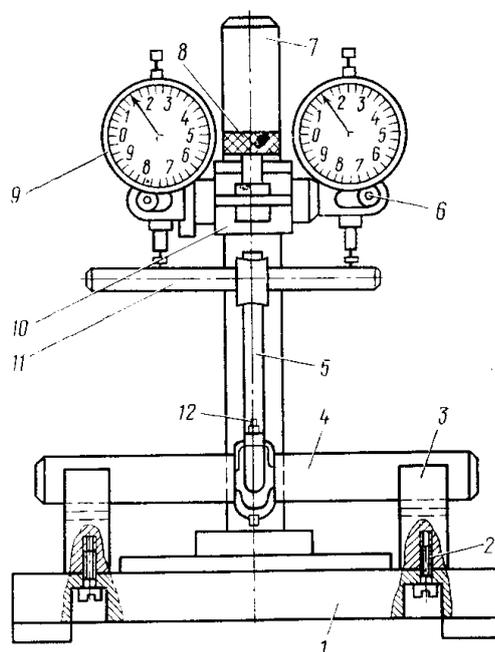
Приспособление для проверки параллельности осей головок шатуна: 1 – основание; 2 – плита; 3 – призма; 4 – проверочная оправка нижней головки шатуна; 5 – шатун; 6 – винт крепления индикаторов; 7 – стойка; 8 – винт крепления хомута; 9 – индикатор; 10 – хомут; 11 – проверочный палец верхней головки шатуна; 12 – болт
